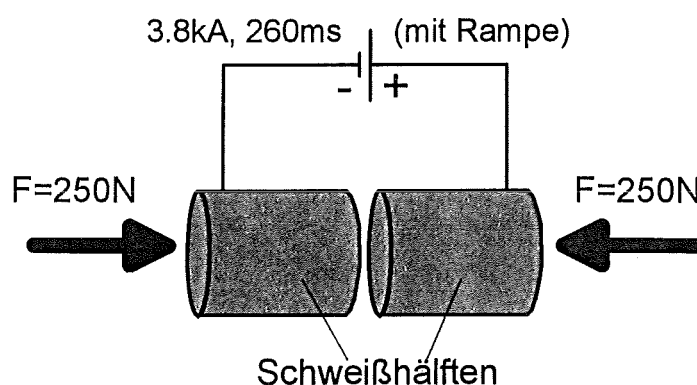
Schemabild zum Widerstands-Stoßschweißen
